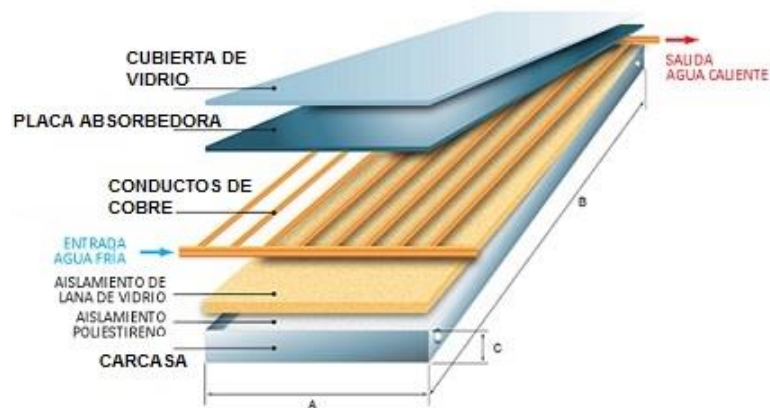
Colector de plato plano con cobertura de vidrio (ingemecánica)
